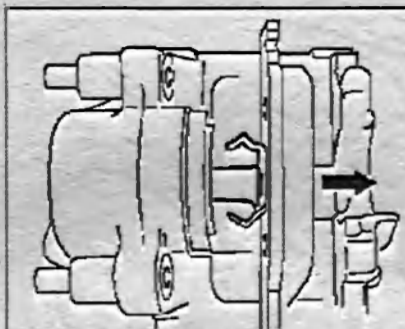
Извлеките тормозную колодку из верхней части тормозного суппорта.
